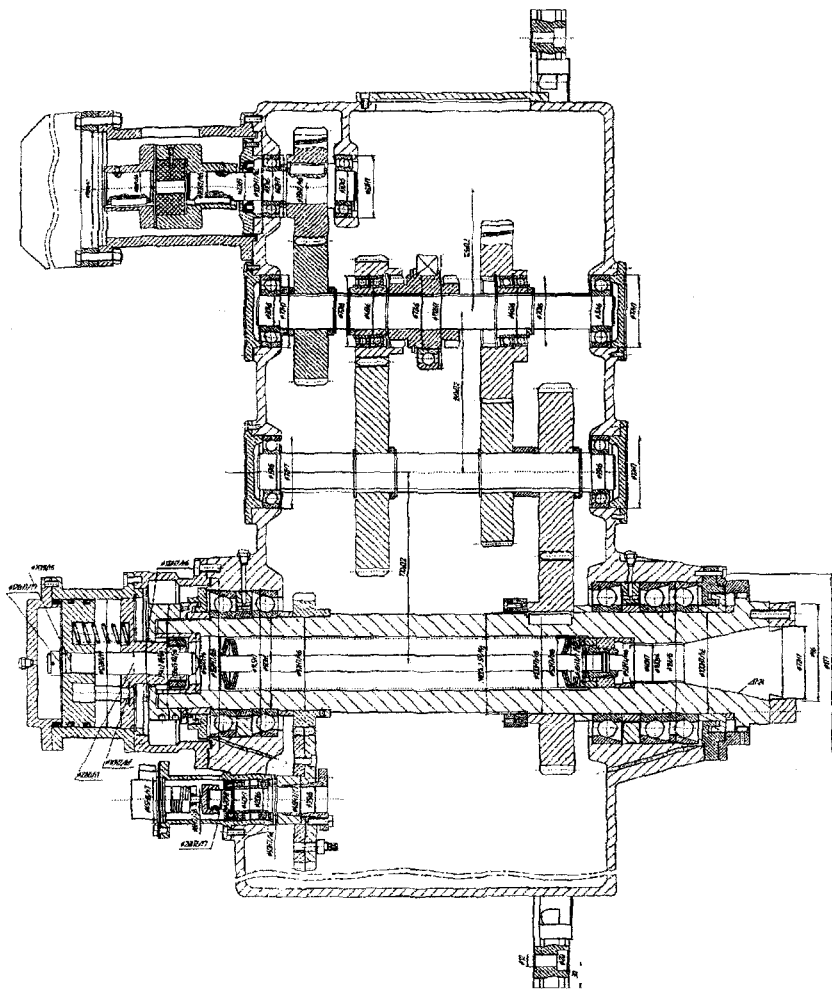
Шпиндельная бабка горизонтального многооперационного станка со встроенным в общий корпус шпиндельным узлом и коробкой скоростей
